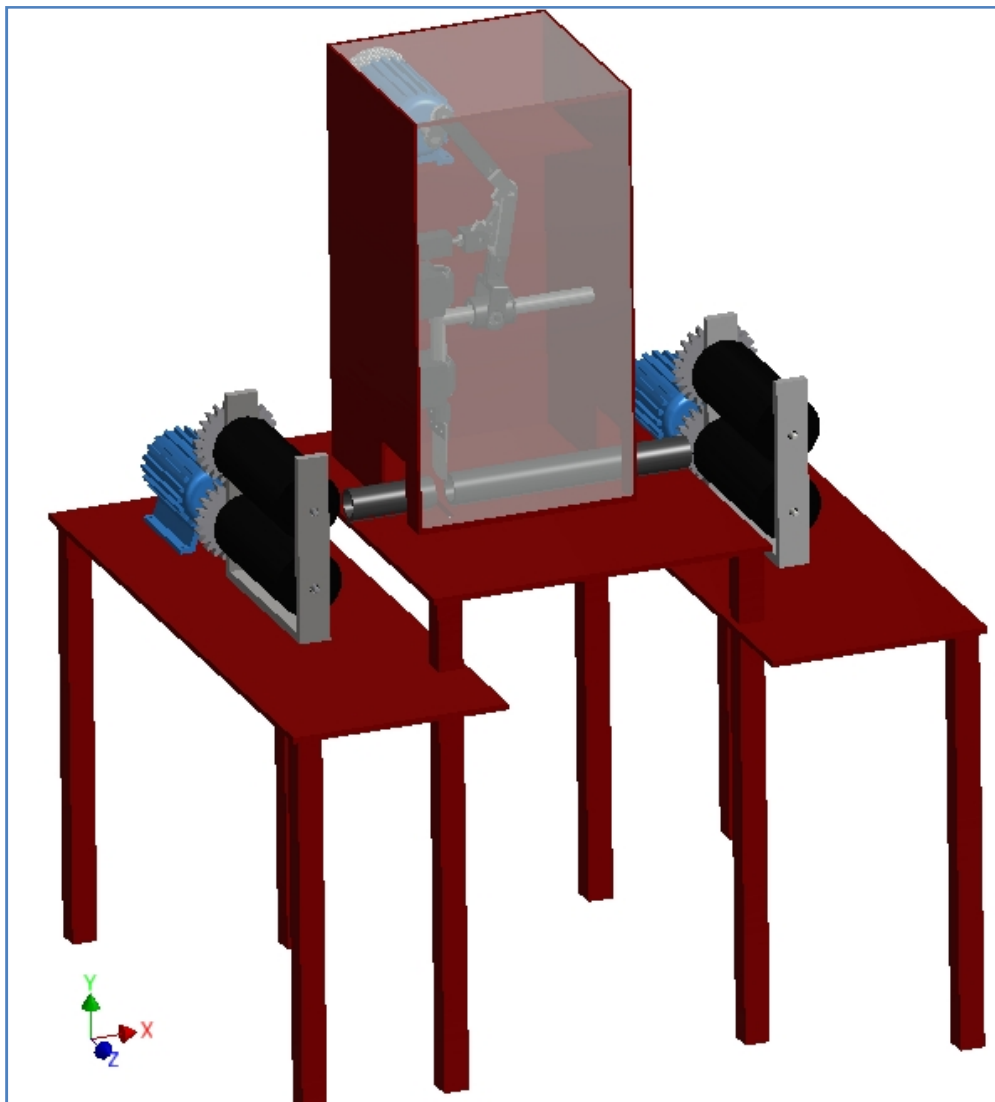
Representación final del ensamblaje de la máquina de corte completa.
